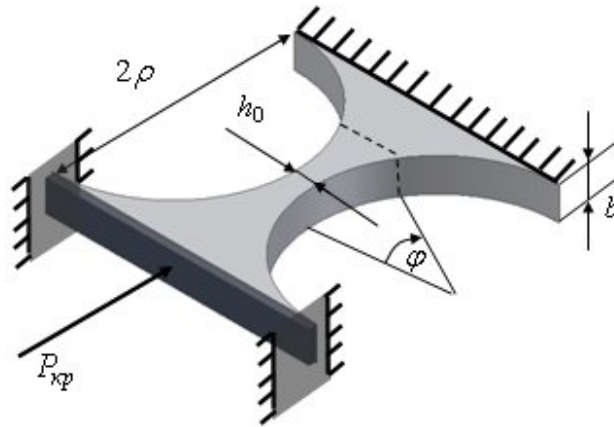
Стержень, образованный двумя цилиндрическими поверхностями
